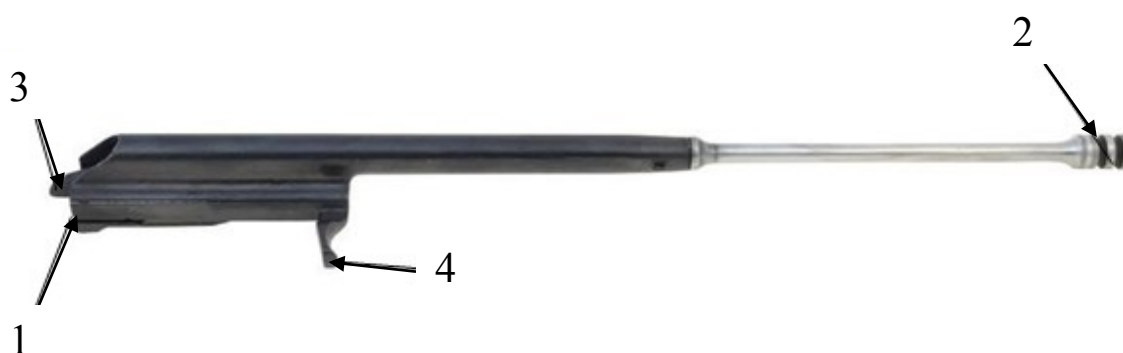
Затворная рама с газовым поршнем: 1 – канал для затвора; 2 – газовый поршень; 3 – предохранительный выступ; 4 – рукоятка
